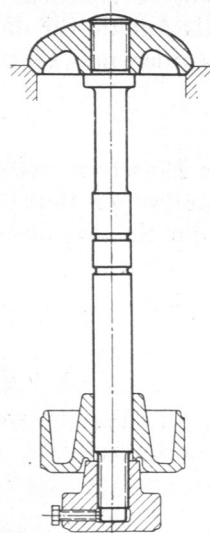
Ungekühltes Großgasmaschinen-Auslaßventil, Ehrhardt & Seher, Schleifmühle, Saarbrücken.
